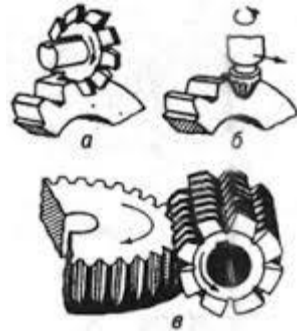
Схема нарезания зубчатых колес методом обката:
